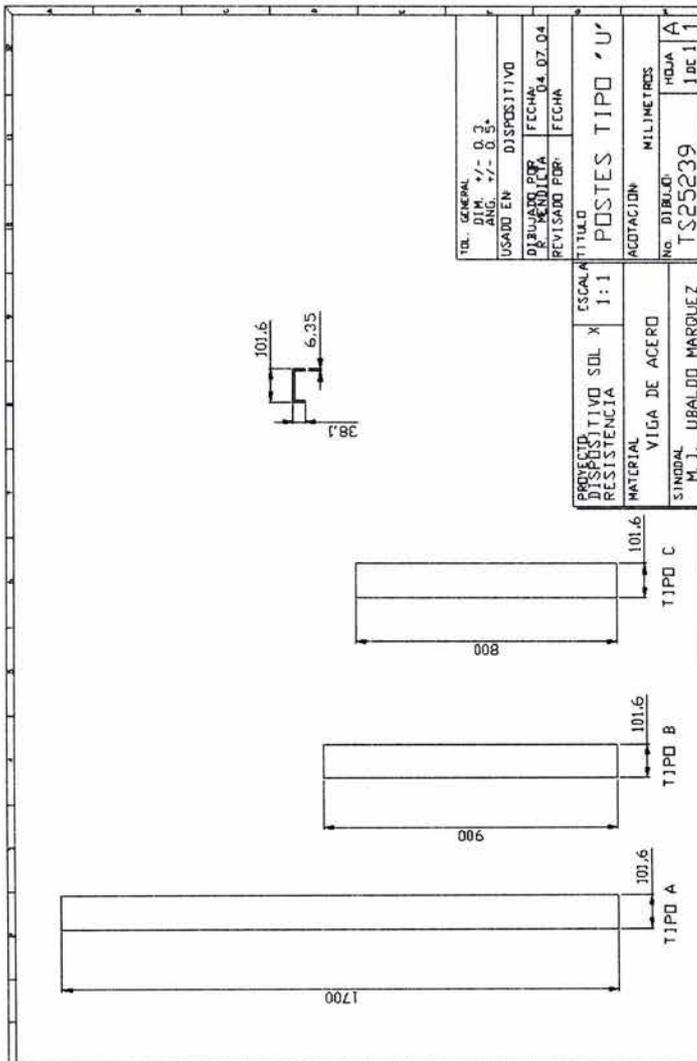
Postes de acero para la estructura de la mesa de trabajo, donde serán montadas las partes que constituirán el dispositivo de soldadura.
